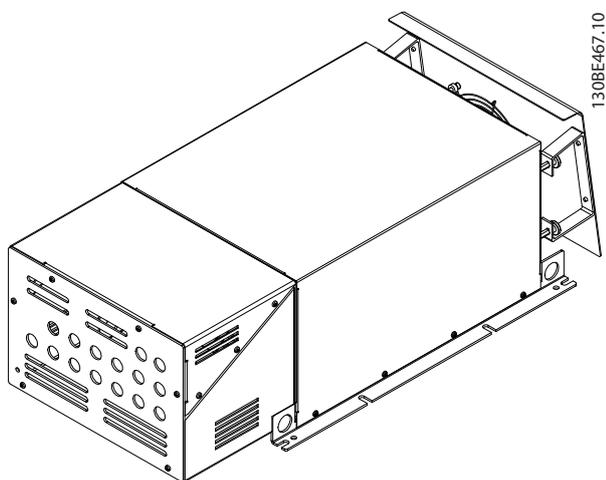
IP21 X3, внешний вентилятор 1, 3D-вид
